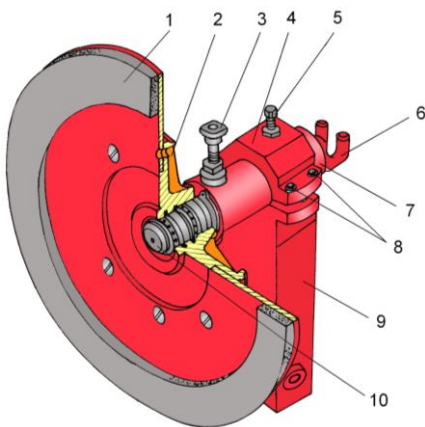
Заточное устройство: 1 – диск заточной; 2 – диск; 3 – стопор; 4 – корпус верхний; 5 – фиксатор; 6 – винт; 7 – корпус; 8 – болты; 9 – стойка; 10 – шток
